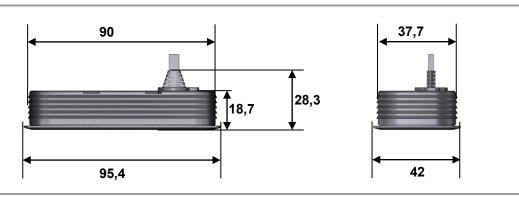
Bedienelement TOUCHinlay, Montagemaße (Angaben in mm)
